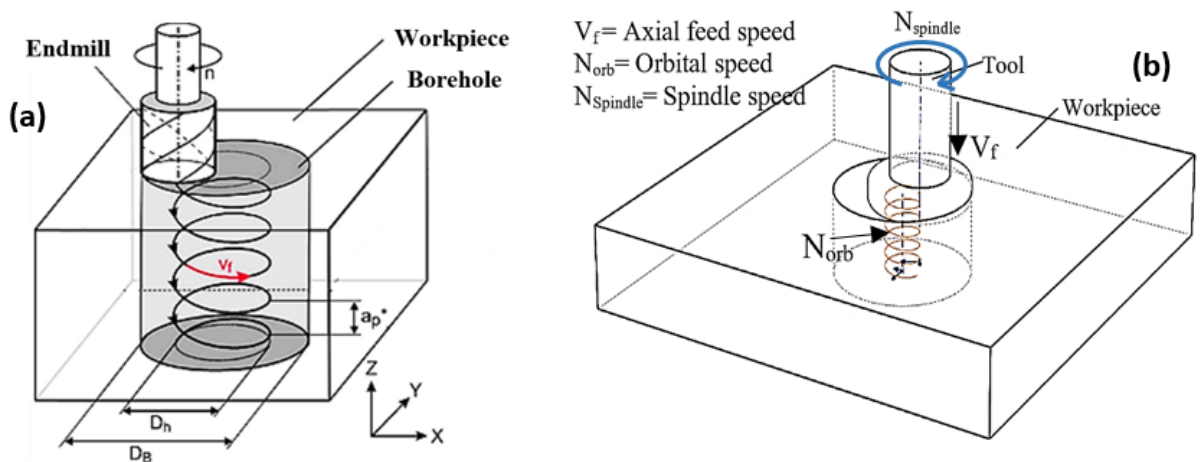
Схеми процесів попередньої обробки поверхні фрезеруванням а) з наступним гвинтовим розкочуванням б) [26]
